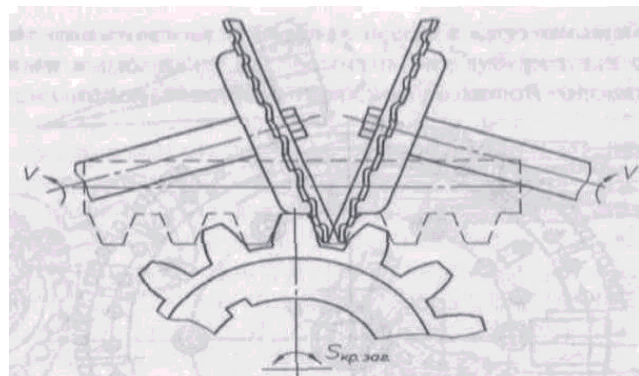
Нарезание зубьев конического колеса двумя дисковыми сборными фрезами
